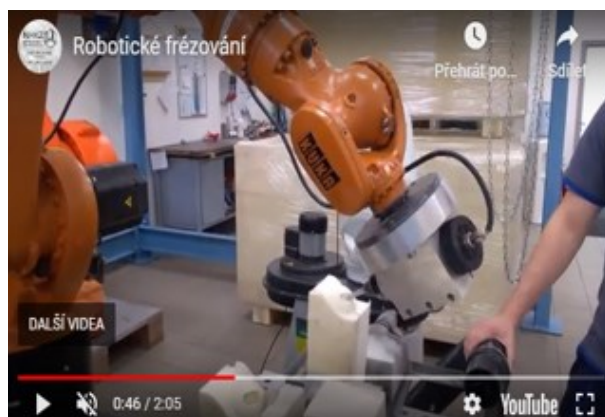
Frézování schodiště pomocí CAD/CAM systému Robotmaster [12]
